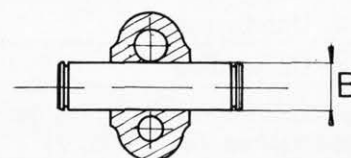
Abmessungen der Buchsen für Kipphebel und Zapfen.
